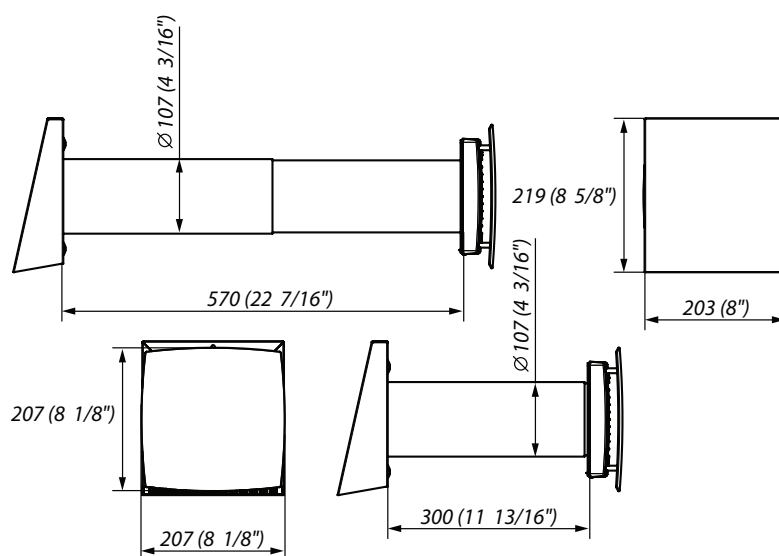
Габаритные и присоединительные размеры агрегата ТвинФреш Комфо РА-25
